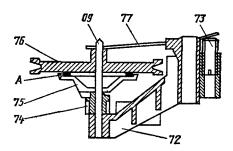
Муфта сцепления ЛПМ магнятолы «Вега-335-стерео»: А — фетровое кольцо; 72 — рычаг муфты сцепления; 73 — стопорный (регулировочный) виит; 74—зубчатая втулка; 75 — фрикционный диск; 76 — диск муфты сцепления; 77 — плоская пружкина; 09 — ось
